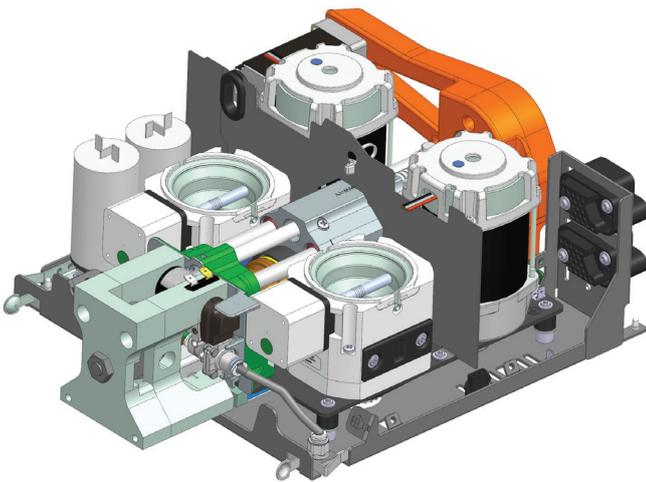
Modul-Aufbau mit Kraftmessvorrichtung
